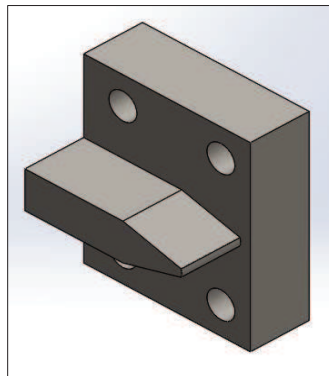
9. DIMENSIONES DE LA PUNTA DEL PERCUTOR
